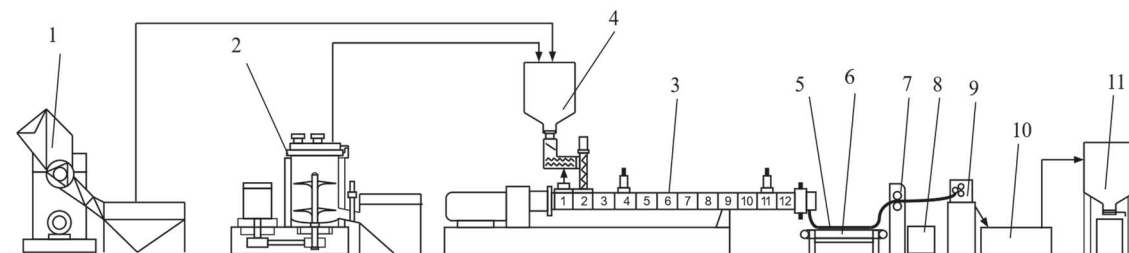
Лабораторна схема виготовлення зразків ПВХ композитів
